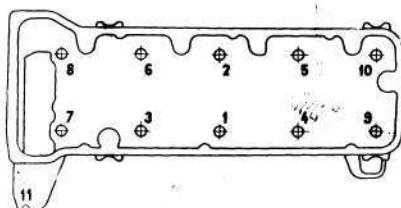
Порядок затягивания болтов крепления головки цилиндров
